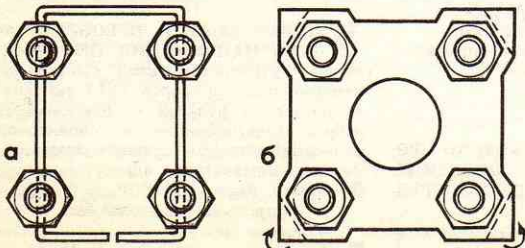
Шплинтовка гаек: а — проволокой; б — общей шайбой.
